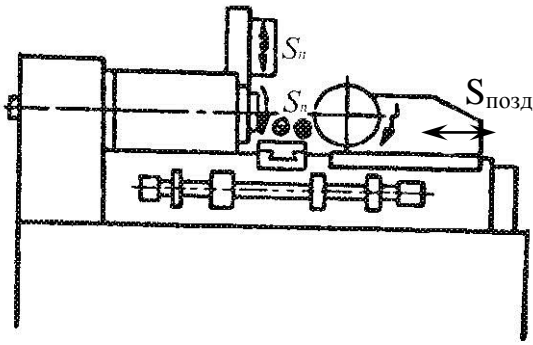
Загальний вид одношпindelного токарно-револьверного автомата
